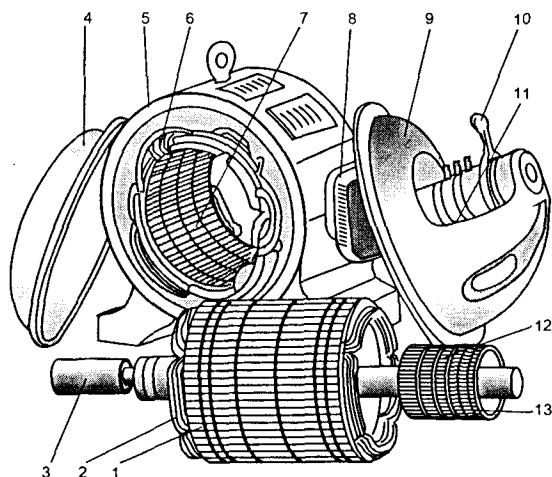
Асинхронный электродвигатель с фазным ротором: 1 — сердечник ротора; 2 — обмотка ротора; 3 — вал; 4 — подшипниковый щит со стороны привода; 5 — корпус статора; 6 — обмотка статора; 7 — сердечник статора; 8 — коробка выводов; 9 — подшипниковый щит со стороны контактных колец; 10 — рычаг короткозамыкающего приспособления; 11 — щеткодержатели внутри щита 9; 12 — контактные кольца; 13 — смещающееся вдоль вала кольцо короткозамыкающего приспособления
